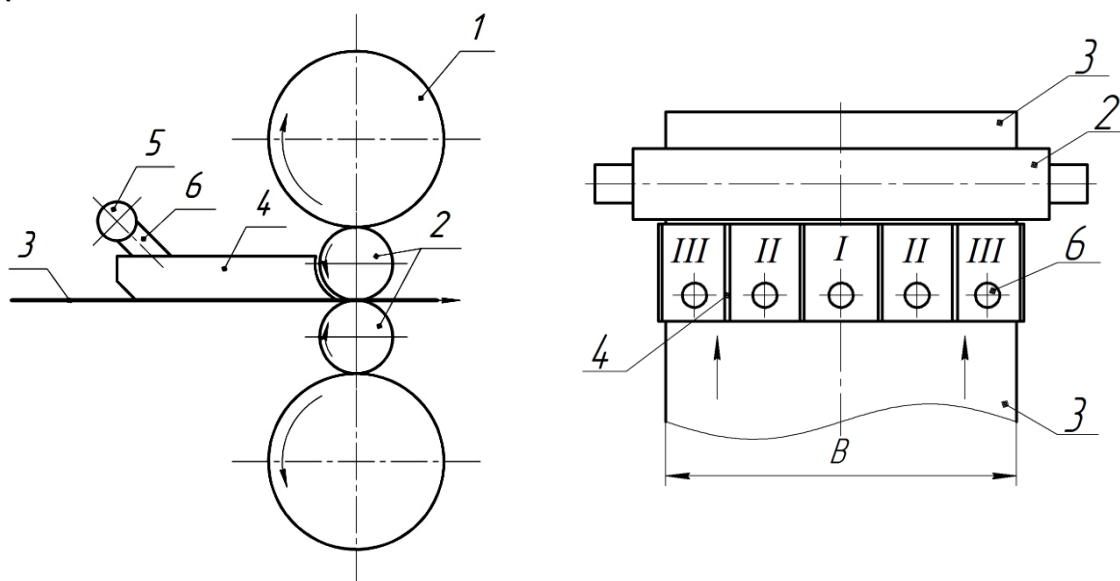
Схема пристрою для диференційованого подання охолоджувача на штабу: 1 - опорний валок; 2 - робочі валки; 3 - штаба; 4 –перегородки ; 5 - колектор; 6 – трубка для подачі охолоджувача
